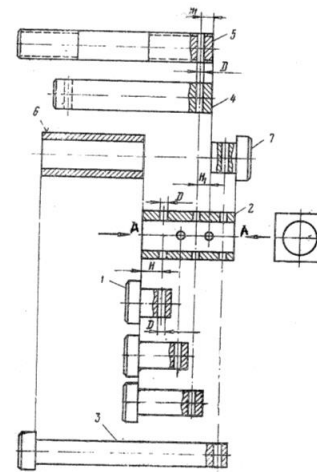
Схема сверления отверстий в осях и шпильках под шплинт с применением универсального кондуктора
